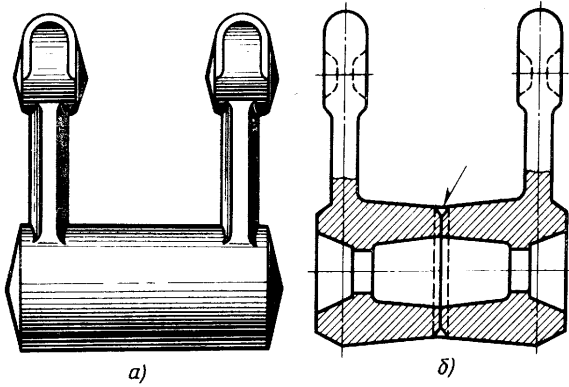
Цельноштампованная (а) и сварная (б) заготовки
